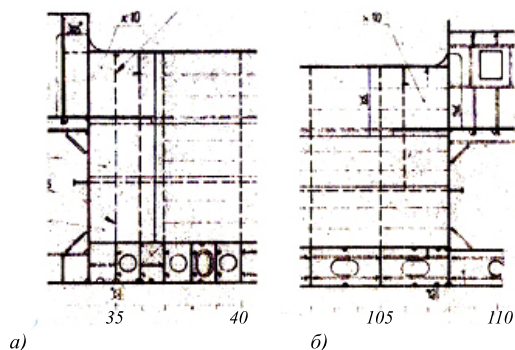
Схема конструктивного окончания: а – юта; б – бака
